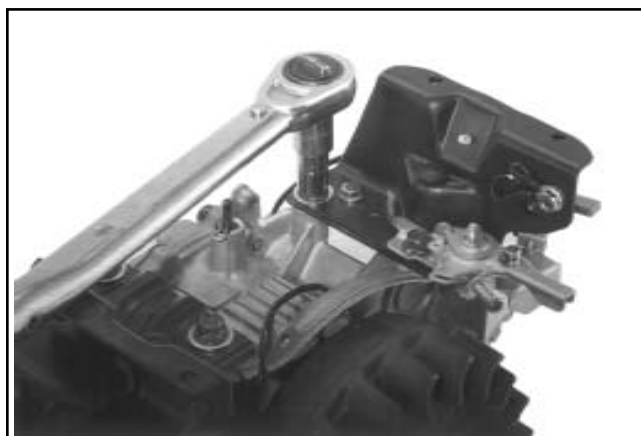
CS6 e CS4. Montaggio del supporto del serbatoio del carburante di destra.
